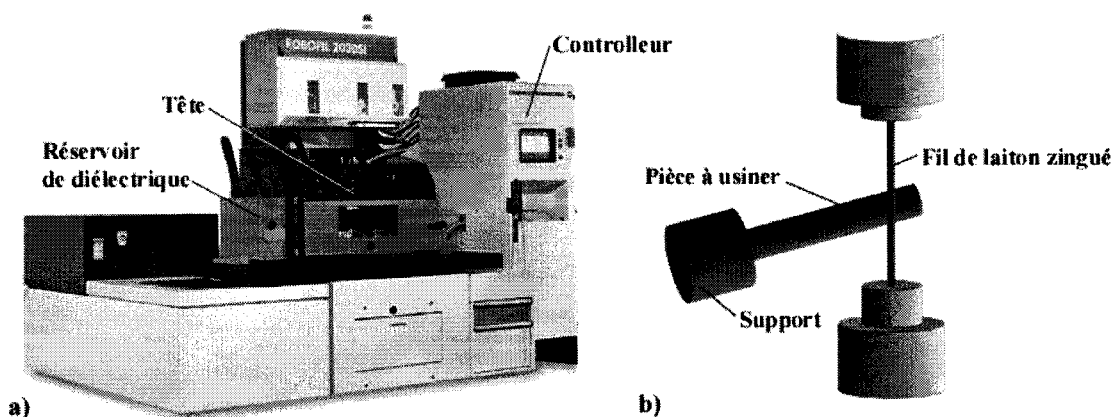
Robofil 2030SI de la compagnie Charmilles [91] a) vue d'ensemble, b) tête d'usinage
